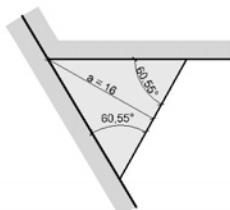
Untersuchte Schweißnahtgeometrien für a = 16mm
